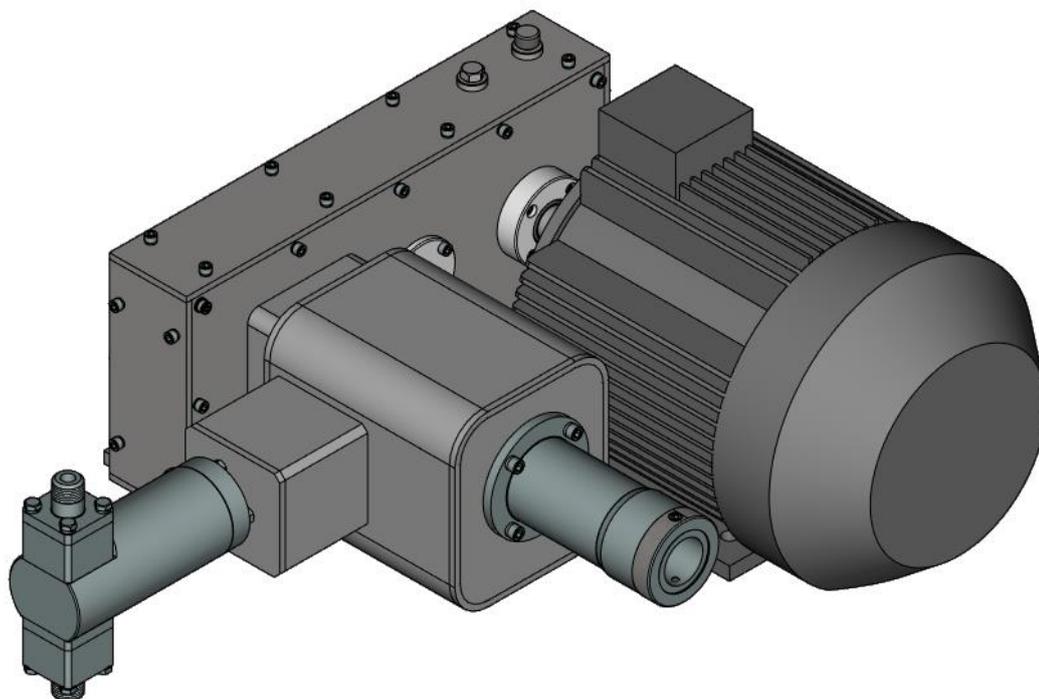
Насосный агрегат дозировочный с цилиндрическим редуктором и блоком регулирования подачи
